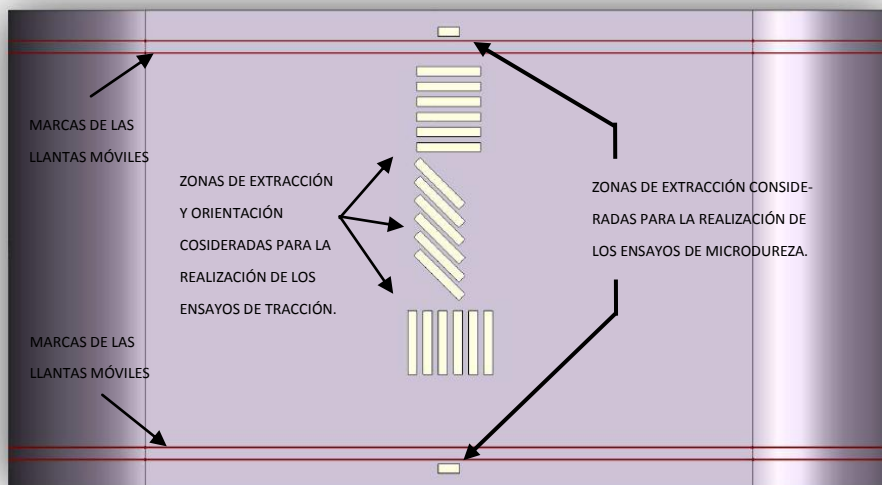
Vista en planta de las zonas de donde se desea extraer las muestras para los ensayos de microdureza y los ensayos de tracción sobre una banda de colada continua Hazelett.
